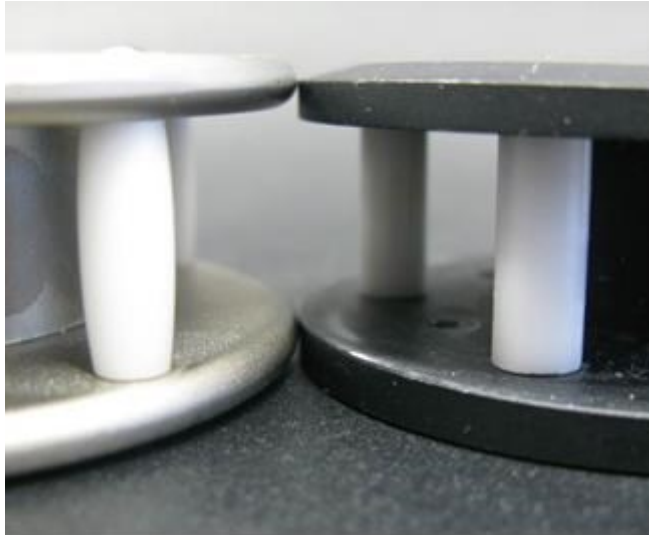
Rodillo convexo a la izquierda y rodillo cilíndrico a la derecha
